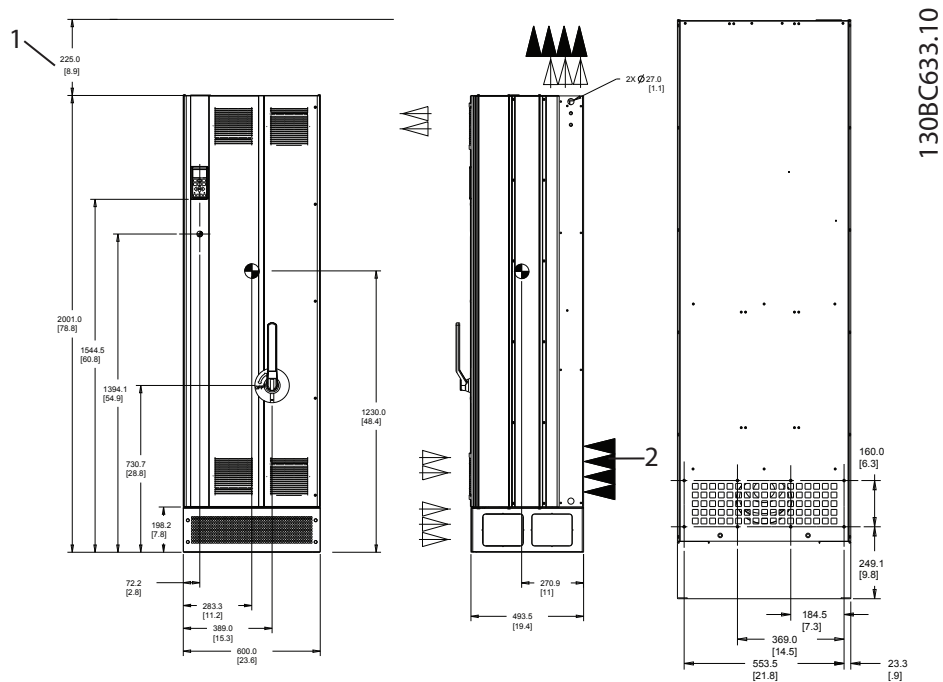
AAF006 250–400 A, размер корпуса E1
